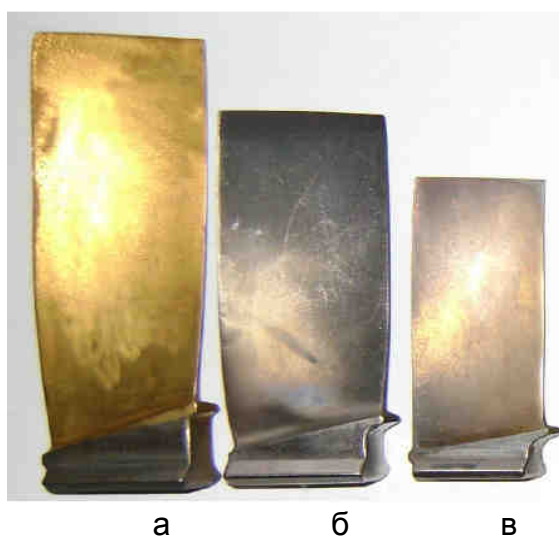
Общий вид лопаток компрессора ГТД модели ТВ3-117:
